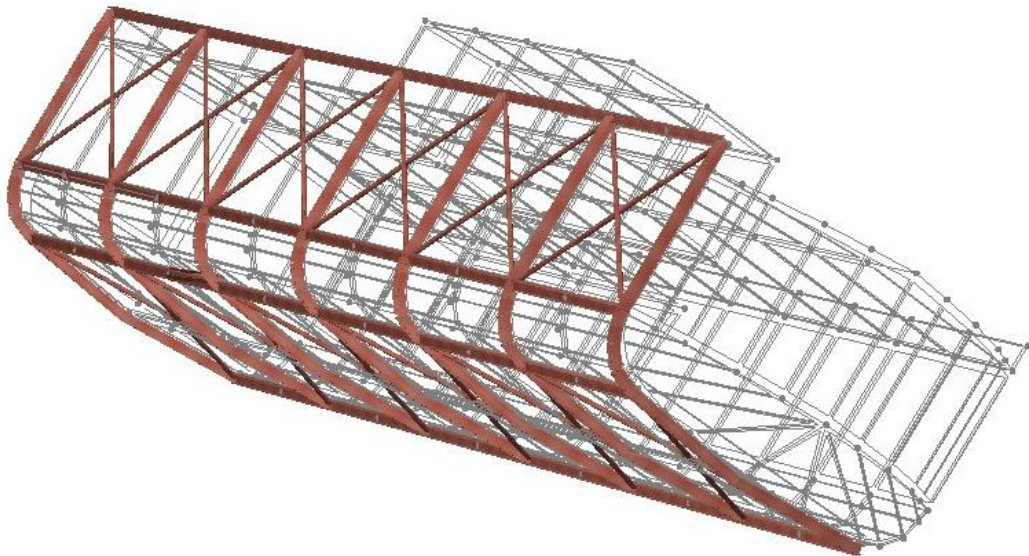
Vista de estructura añadida a RAM Poderoso.
